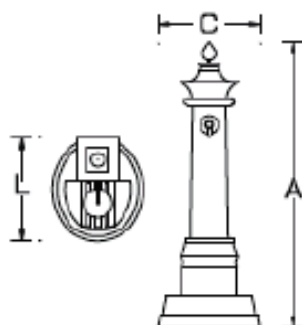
Croquis de Fuente Torre. (Fuente: <http://www.bricantel.pt/es/>)
